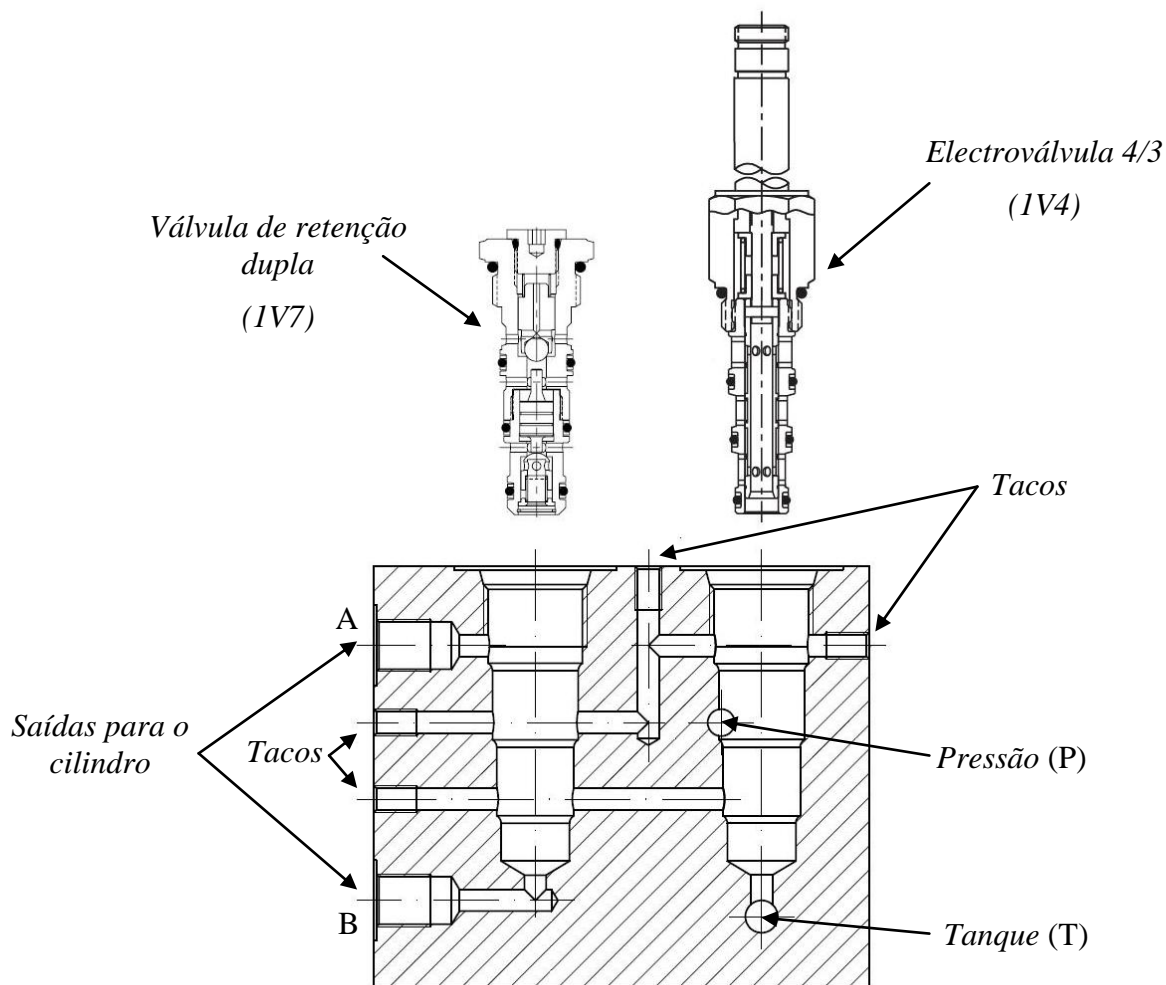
Vista em corte com as válvulas de comando do cilindro da articulação
